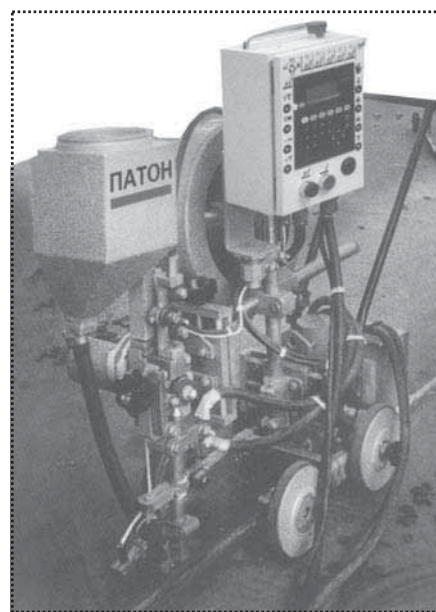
Сварочный трактор Патон ТС-77М
